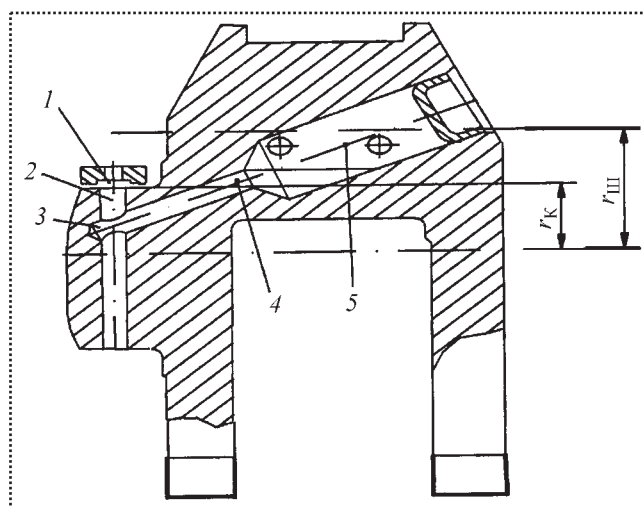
Схема смазки шатунного подшипника двигателя КамАЗ:
